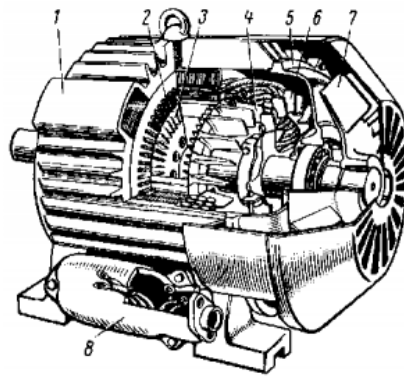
Асинхронний двигун з короткозамкненим ротором: 1 - остов; 2 - статор; 3 - ротор; 4 - стрижні обмотки ротора; 5 - підшипниковий щит; 6 - вентиляційні лопатки ротора; 7 - вентилятор; 8 - коробка виводів
